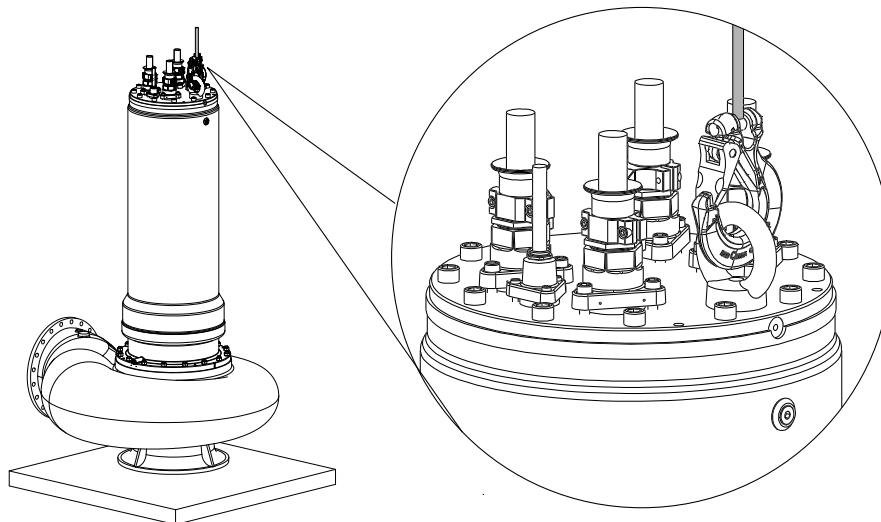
Транспортировать насосный агрегат только с помощью строповочных приспособлений
